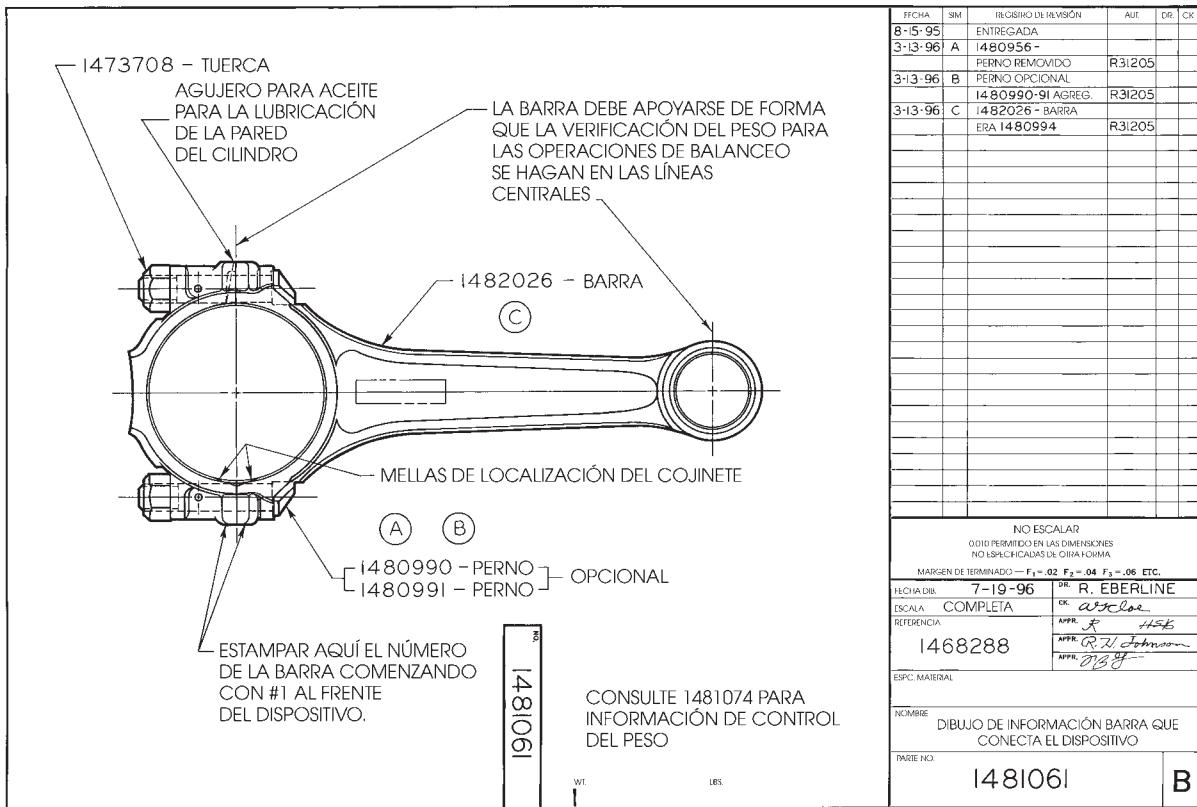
Dibujo de ensamble de una barra de conexión. Cortesía de Cadillac Motor Car Division.
